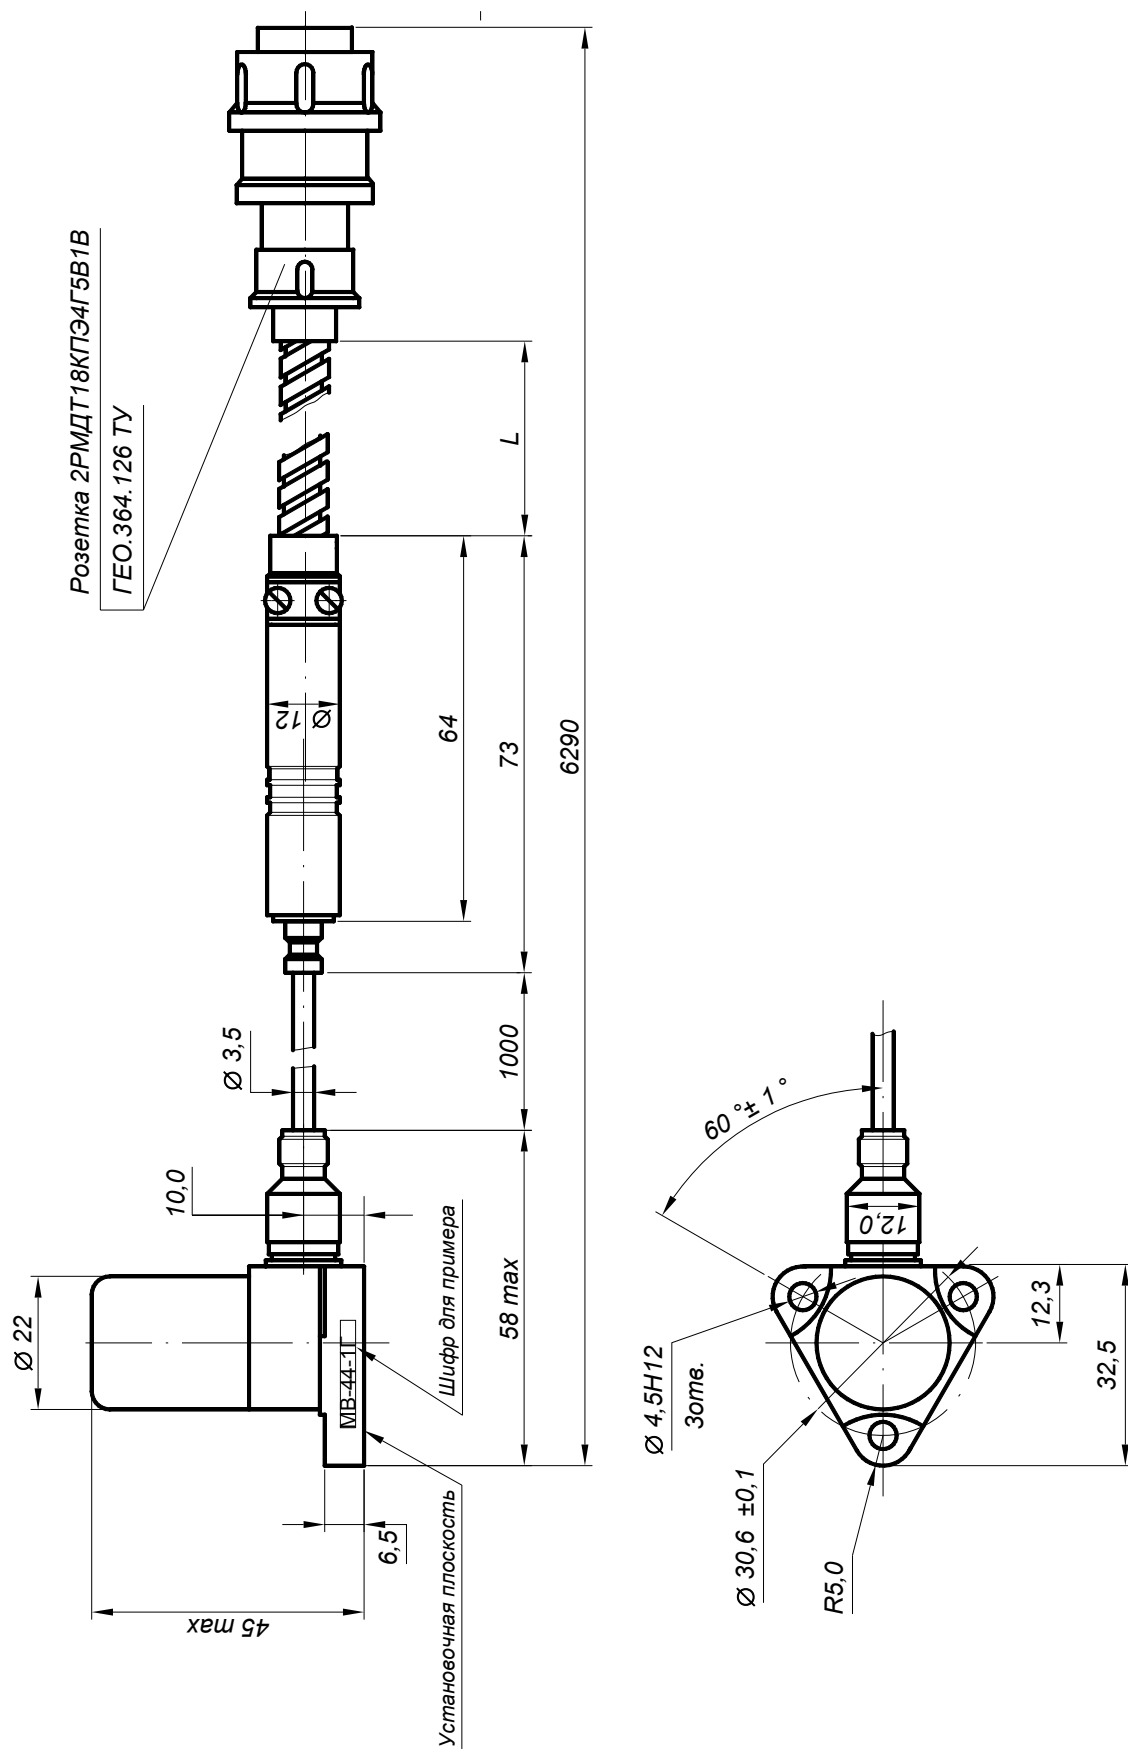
Габаритно-установочные размеры вибропреобразователя МВ-44-1Г/1,0/Л
